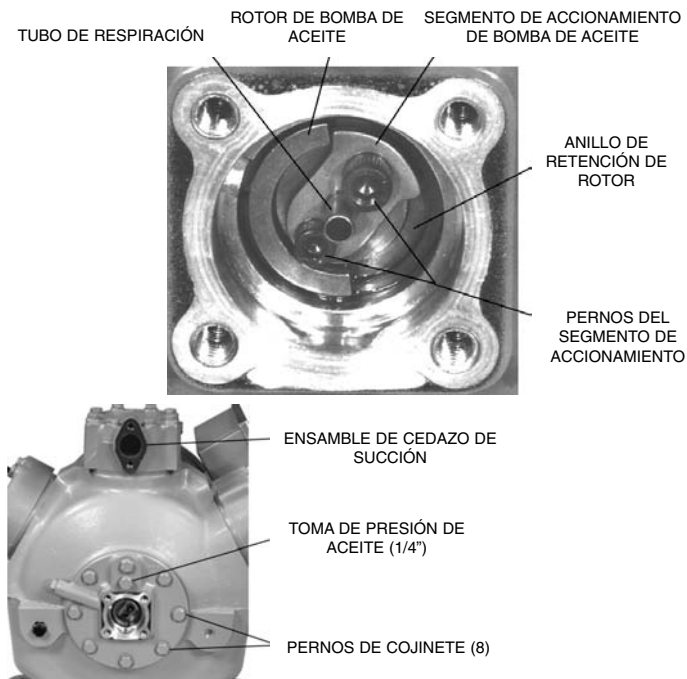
Cómo Retirar la Cabeza de Cojinete del Extremo de Bomba (Compresor 06D)
